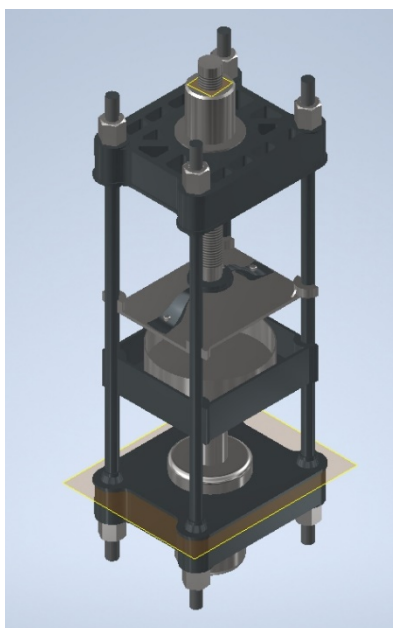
Planos de trabajo para las restricciones de contorno.
